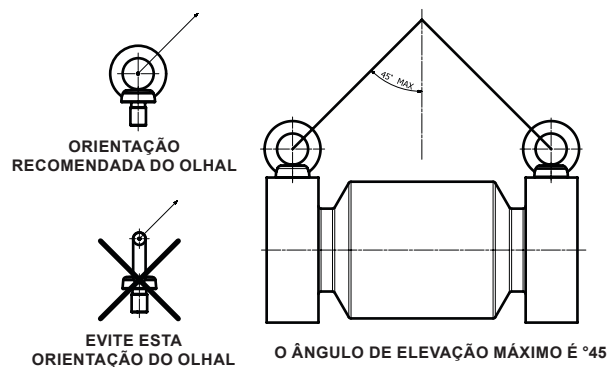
Olhais de elevação: Ilustração de carregamento lateral
